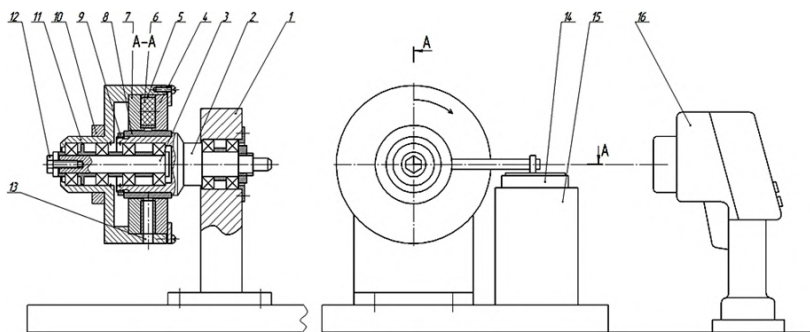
Схема экспериментальной установки: 1 – стойка; 2 – подвижный вал; 3 – неподвижный вал; 4 – съемный полюс; 5 – диск (обойма); 6 – магнит; 7 – съемный полюс; 8 – сменная втулка; 9 – гайка; 10 – хомут; 11 – корпус; 12 – болт; 13 – отверстие для измерения температуры; 14 – весы; 15 – стойка; 16 – тепловизор.
